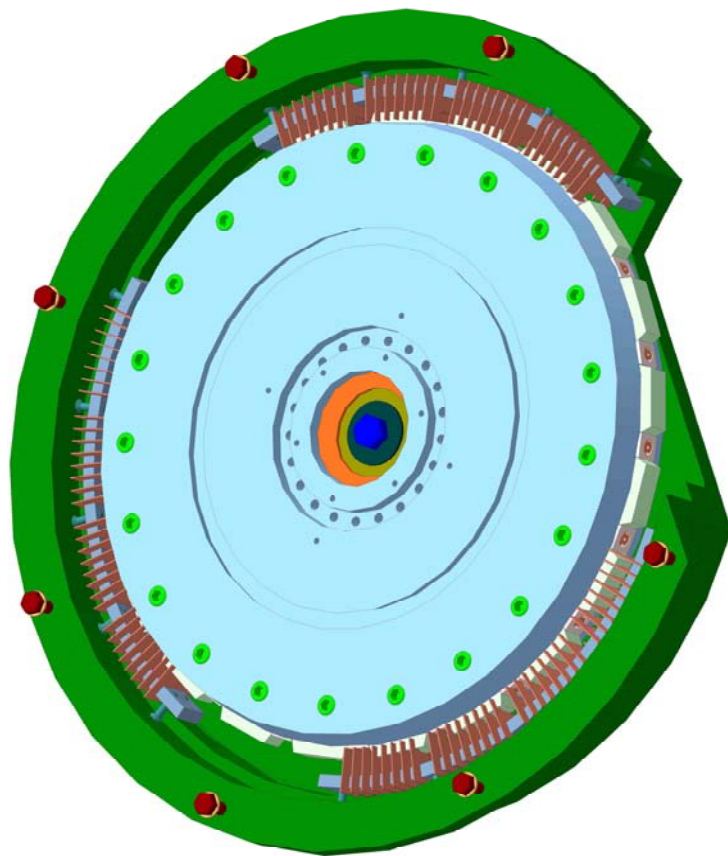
3D-модель модуля сборного шлифовального круга
